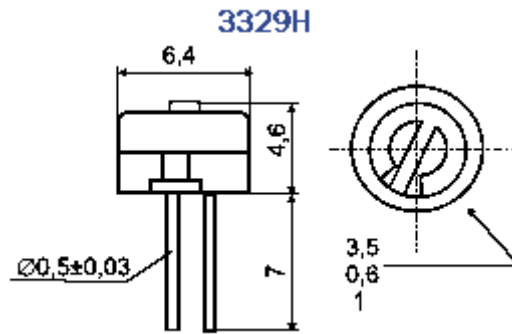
Габаритні розміри резистора підстроювального
